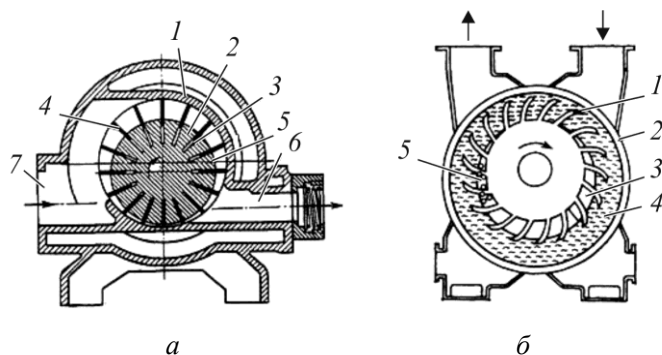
Роторно-пластинчатый (а) и жидкостно-кольцевой (б) компрессоры
